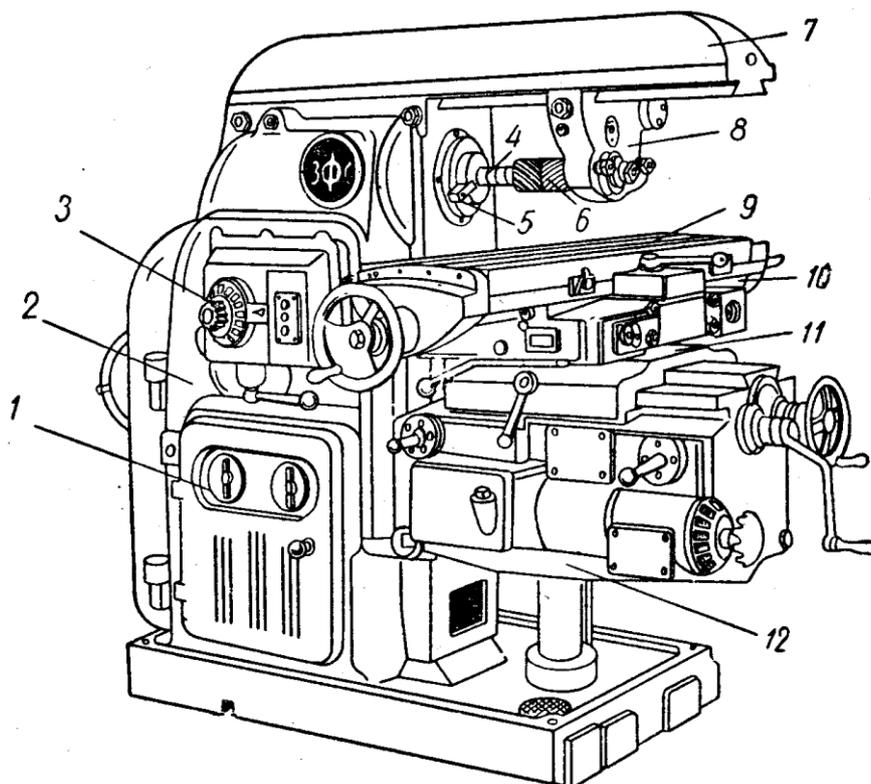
Общий вид горизонтально-фрезерного станка: 1 – коробка подач; 2 – станина; 3 – коробка скоростей; 4 – оправка; 5 – шпиндель; 6 – фреза; 7 – хобот; 8 – дополнительная опора; 9 – стол; 10 – поворотная часть; 11 – салазки; 12 – консоль
